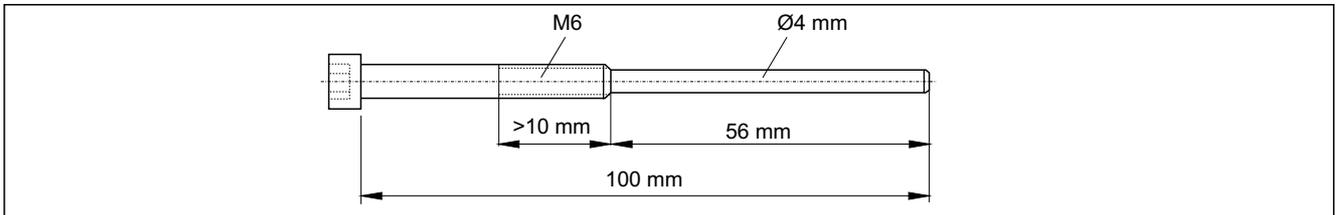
Sonderschraube für Demontage ERN 1381.001 und ROD 431.001
